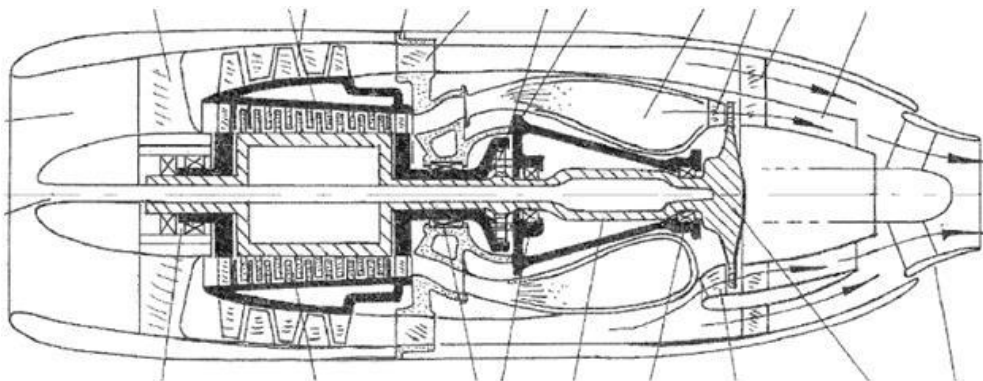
Принципова конструктивна схема двигуна DB 6001
